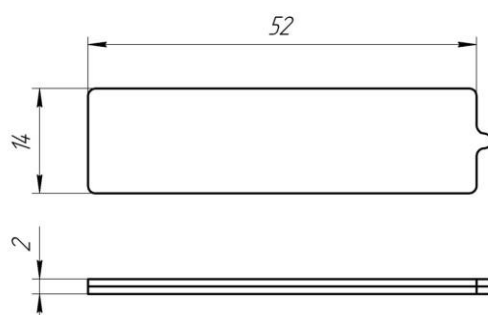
Габаритные размеры и внешний вид ПТТ
